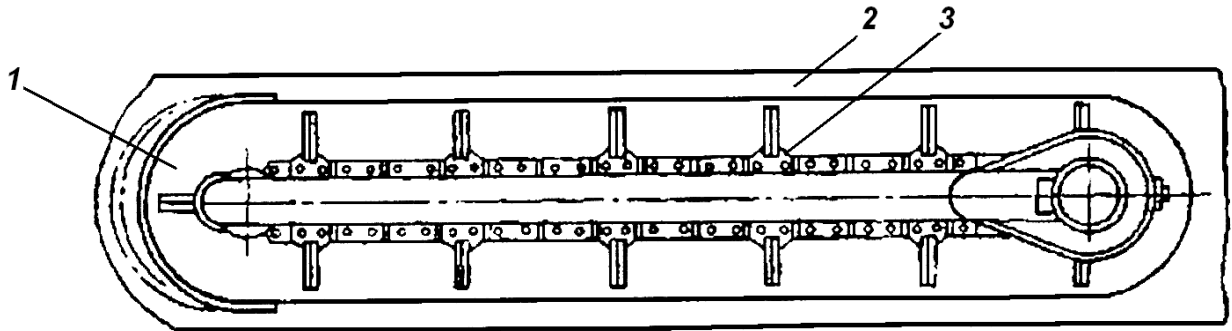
Конструктивна схема скребкового кормороздавача КРС-Φ-15А:
